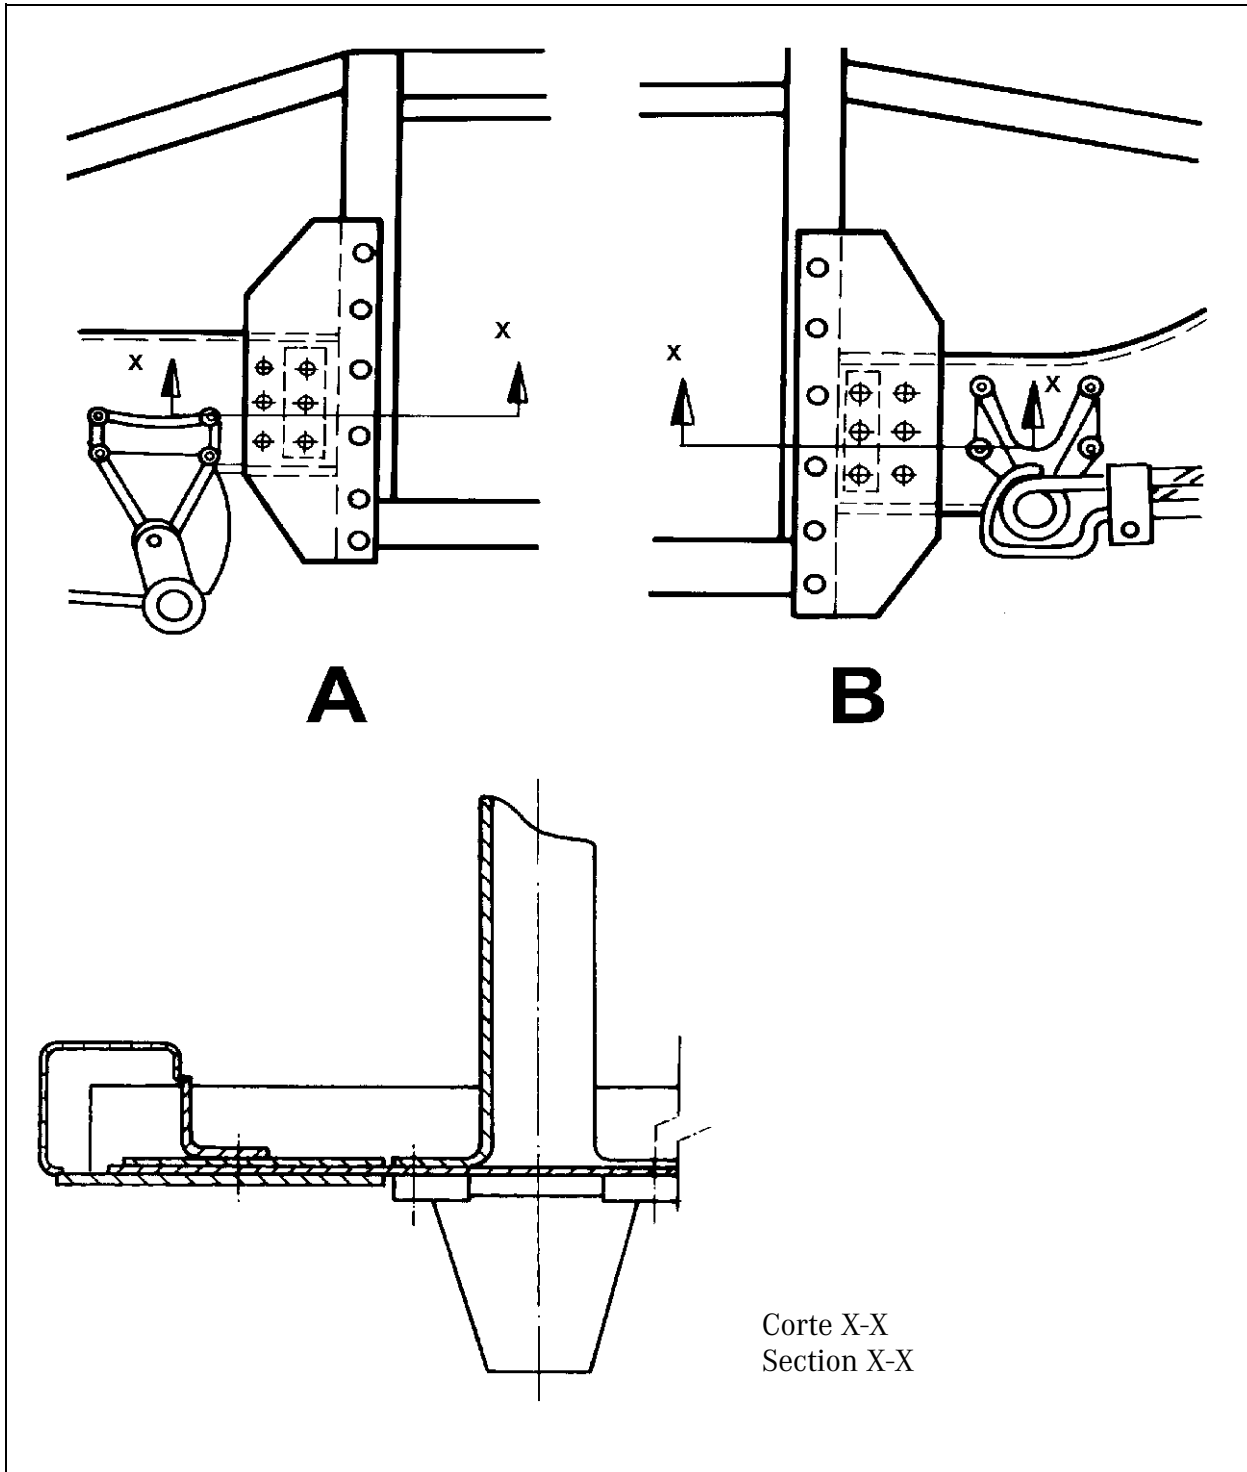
Detalle de la fijación de la estructura central reticulada (ejemplo)
